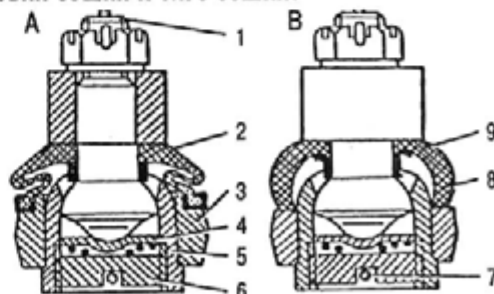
Шариковые шарниры тяг рулевой трапеции: 1 - шаровой палец; 2 - резиновый уплотнитель; 3 - тяга; 4 - опорная плита; 5 - корпус шарнира; 6 - заглушка; 7 - шплинт; 8 - уплотнитель тяги сошки и маятникового рычага; 9 - распорная втулка; А - шарнир наконечника и средней тяги рулевой трапеции; В - шарнир тяги сошки
